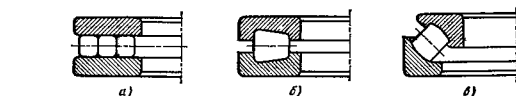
Роликоподшипники упорные типов: а — 9000; б — 19000; в — 39000
